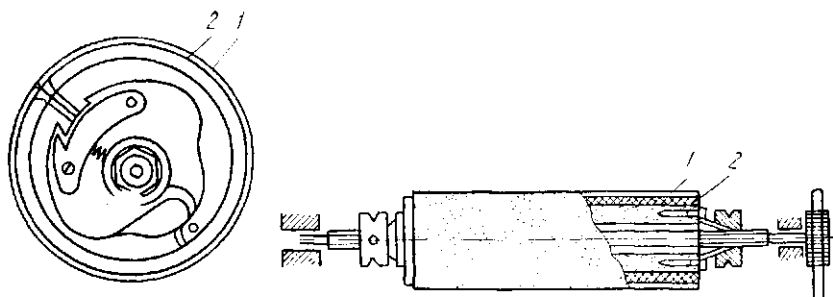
Конструкции рабочих инструментов машины для шлифования
